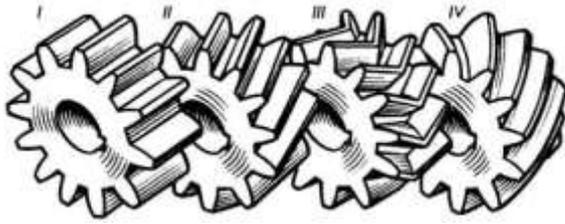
Зубчатые колеса: прямозубые, косозубые, шевронные, с круговыми зубьями
